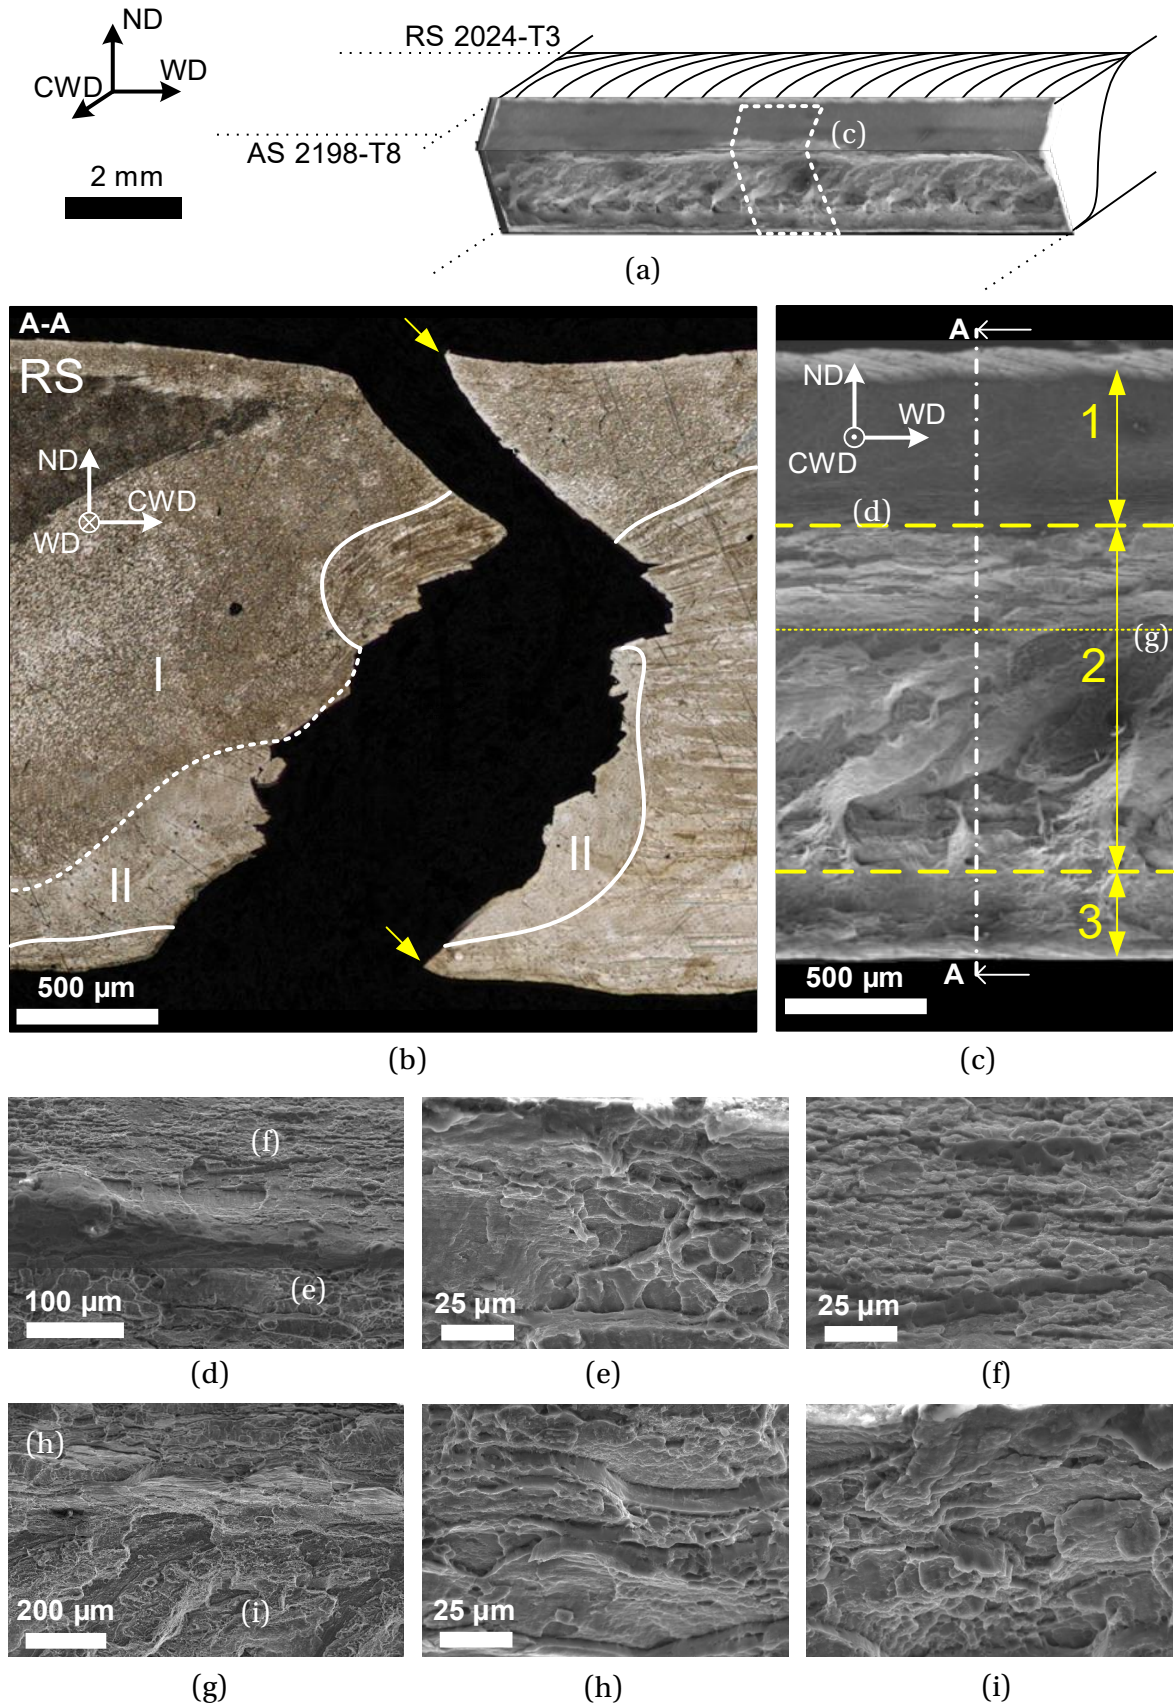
Fractographie macro-éprouvette D-4 5 (a) image globale (MEB), (b) section transverse A-A, (c) surface de rupture (MEB), (d-i) grossissements de (c) (MEB).
